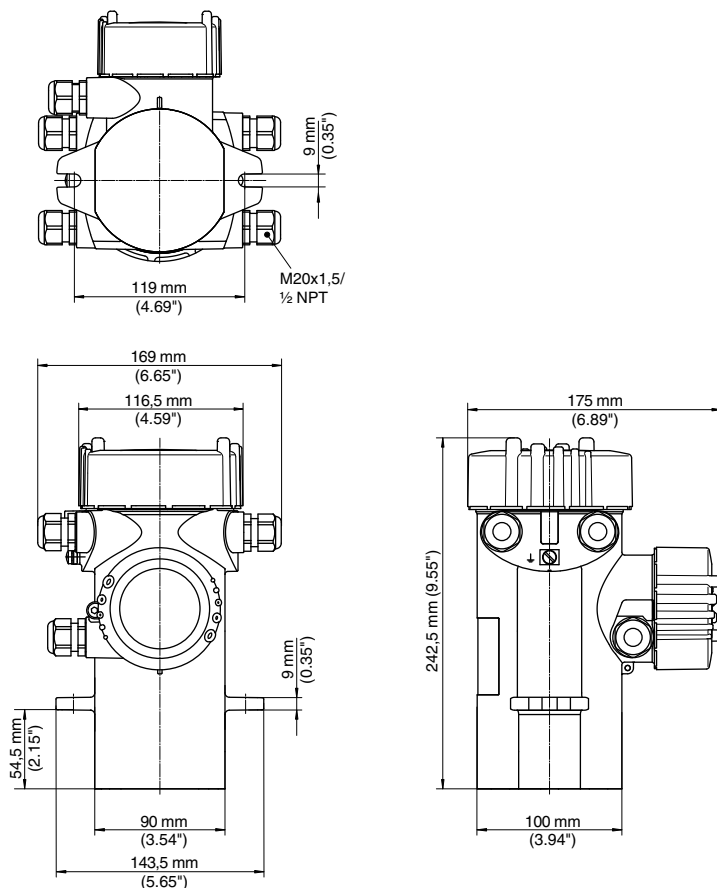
Корпус из алюминия или нержавеющей стали (точное литье)
